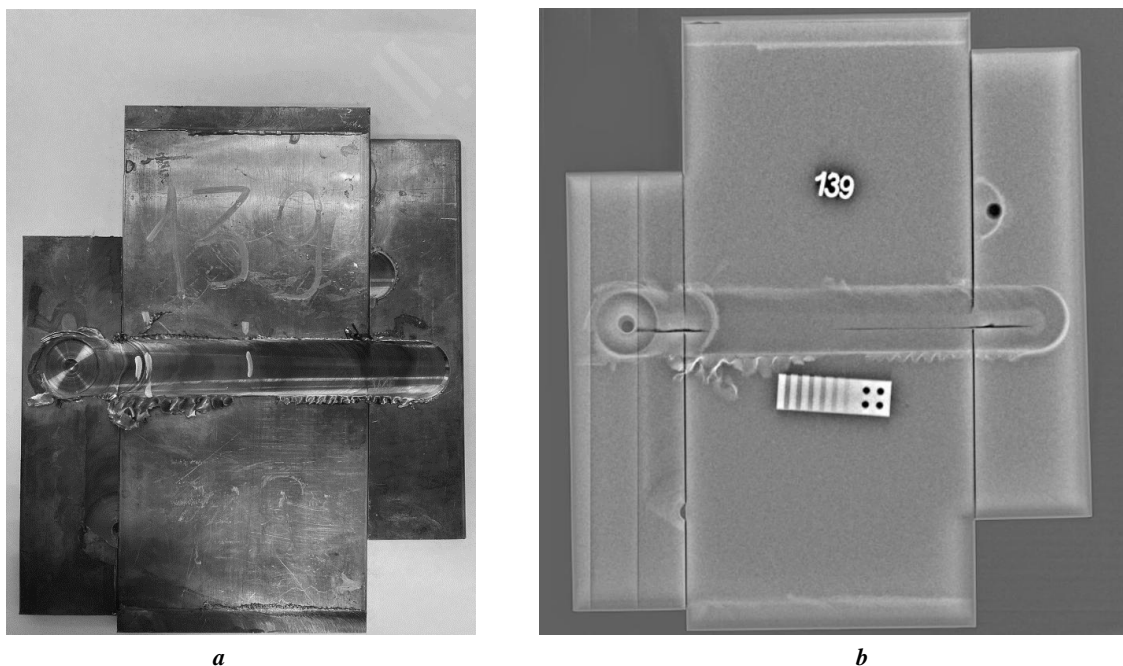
Сварное соединение для механических испытаний: a – внешний вид; b – радиографический снимок
